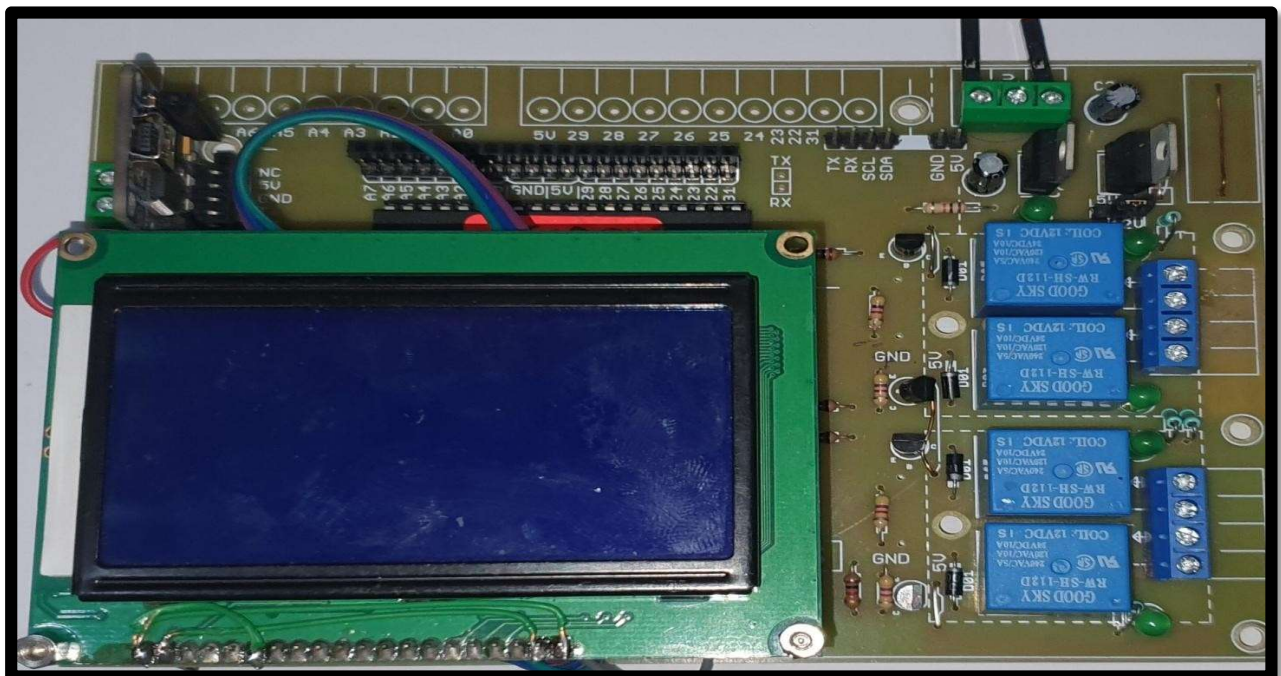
Carte Plc fr 2025 VO1 après le soudage des composants
